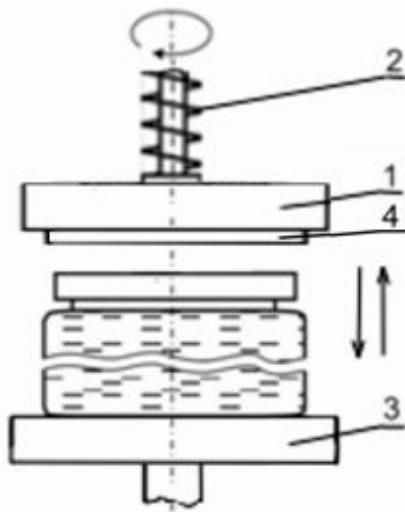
Схема механізму закупорювання машини шайбового типу.
